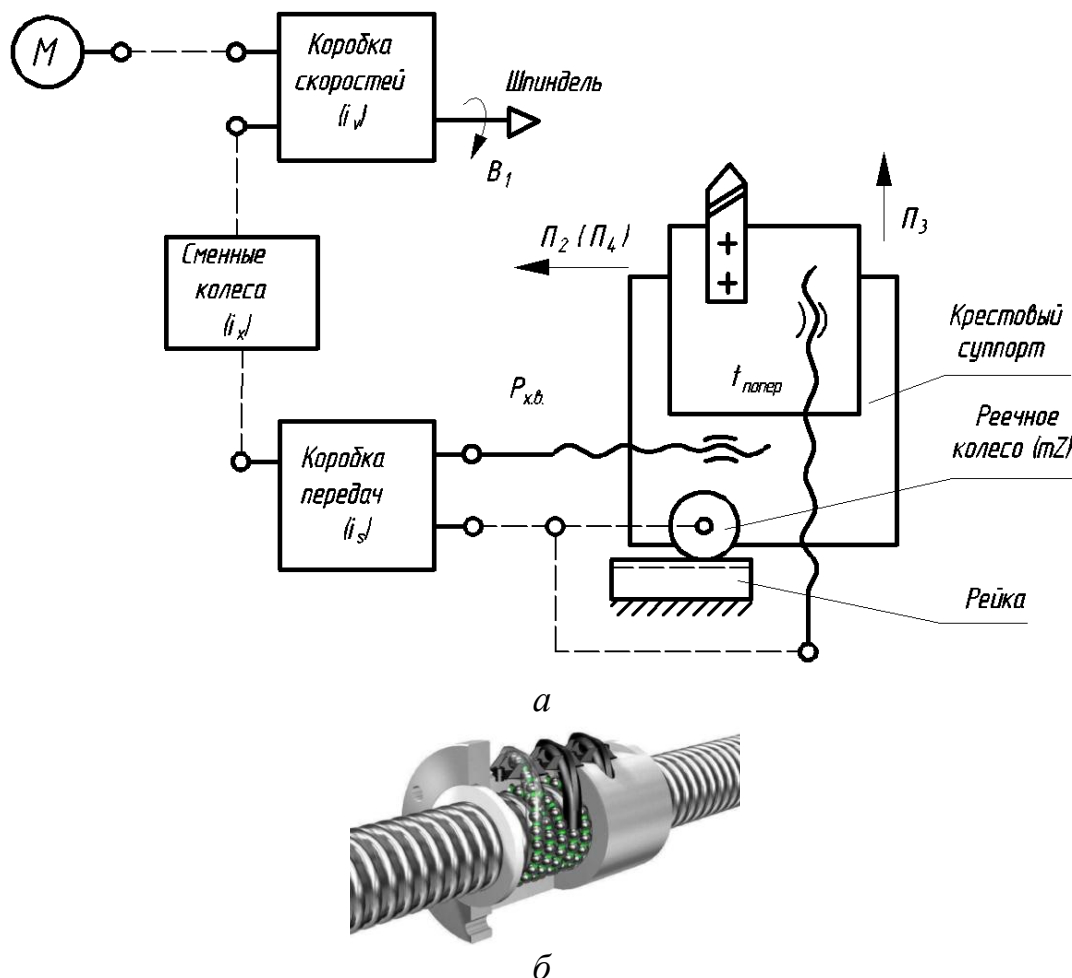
Структурная схема токарно-винторезного станка (а) и ШВП (б)
